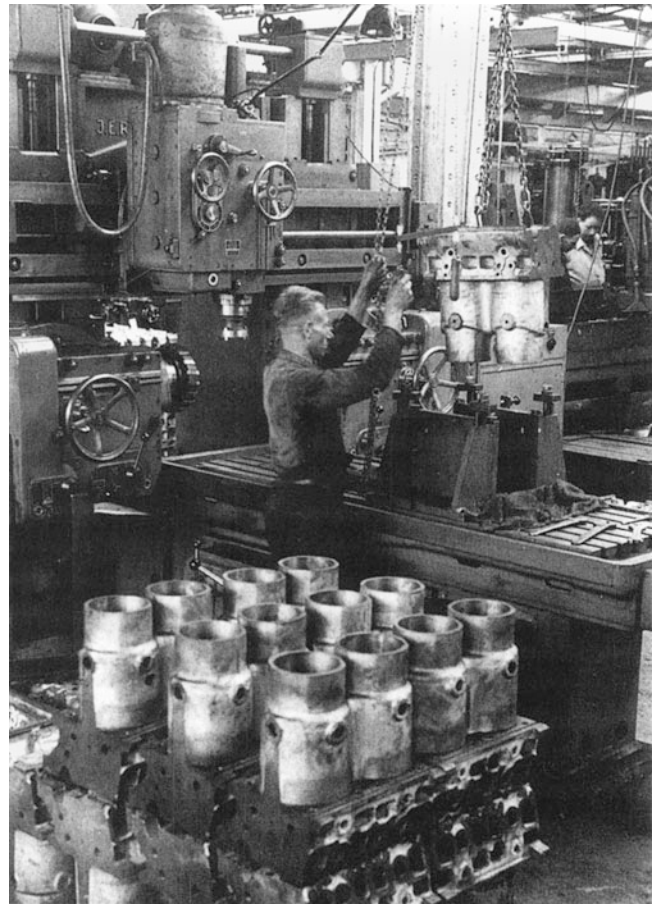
Mechanische Fertigung im Maybach-Motorenbau: Fräsen der Auflageflächen von Blockzylindern für GTO-Motoren
